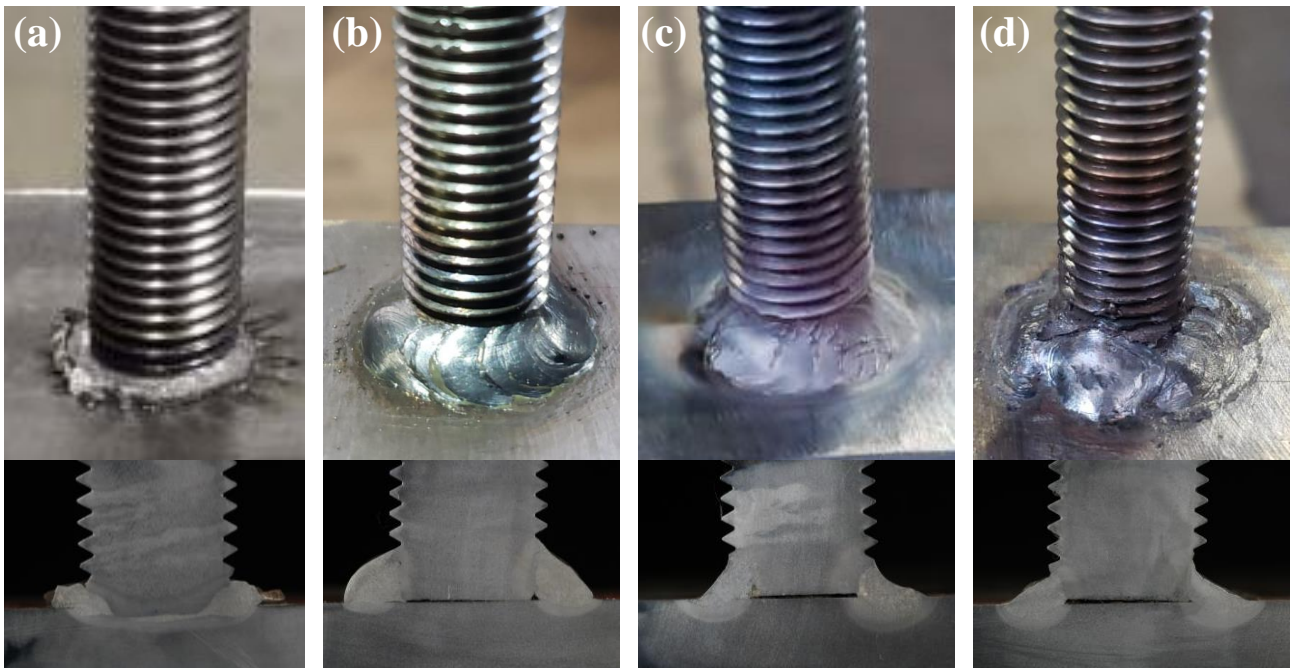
Macrografia dos pinos M16 soldados com diferentes processos de soldagem:
